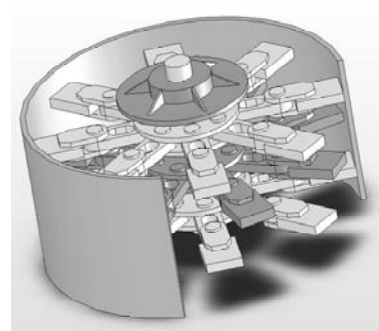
Конструктивная схема дробилки ударного действия с вертикальным ротором
